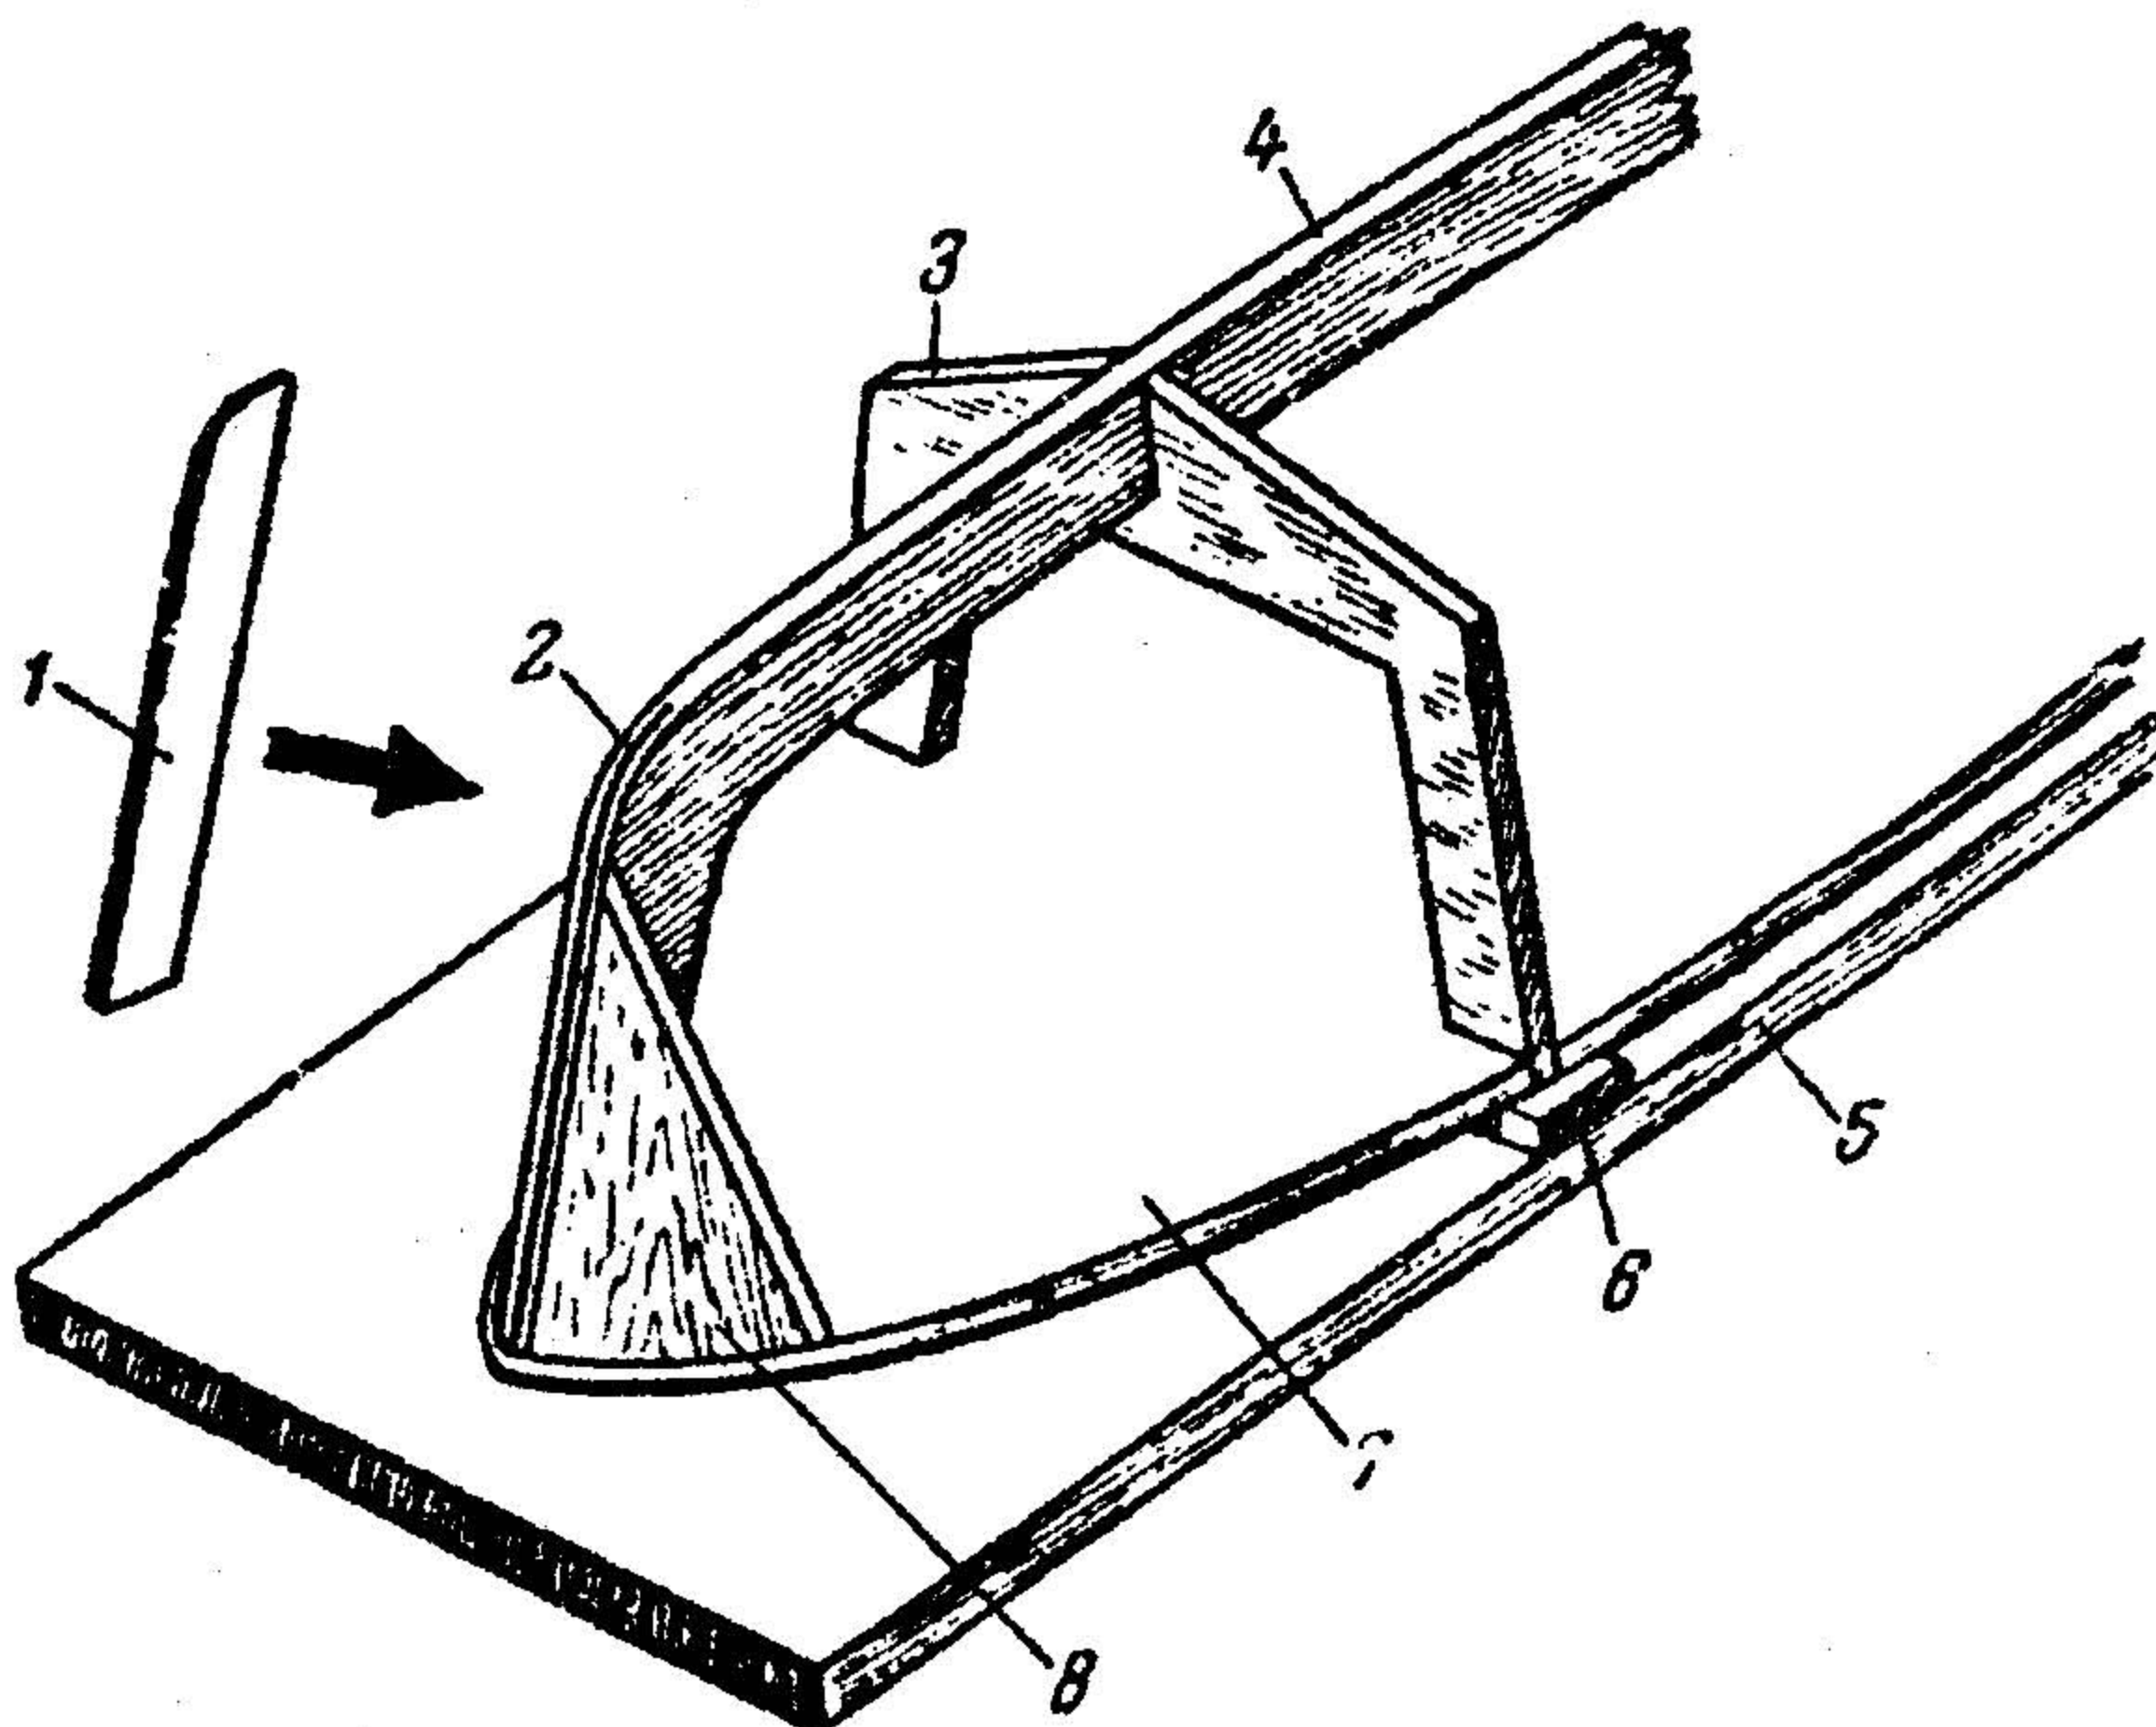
Установка носовой оковки: 1 — носовая оковка; 2 — щель для носовой оковки; 3 — шпангоут; 4 — килевая рамка; 5 — стоечная доска; 6 — стоечный брус; 7 — настил палубы; 8 — носовая бобышка
